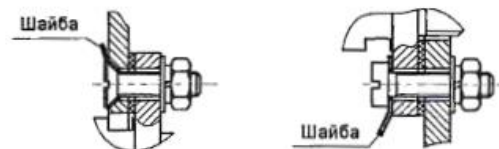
Вариант установки шайб для контровки, пломбировки соединителя СКЦ102
